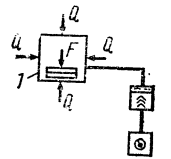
Принцип сварки (I — изделие)
